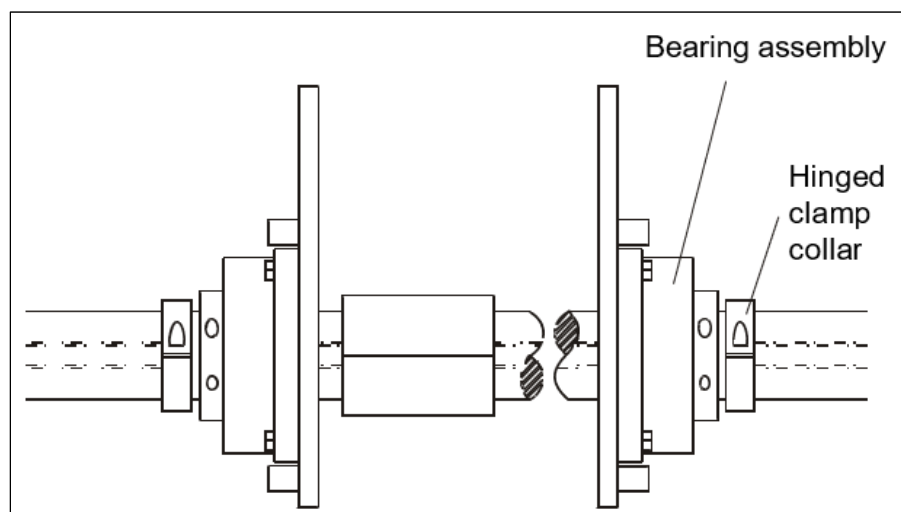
ENSEMBLE SUPPORT DE PALIER DE MONTAGE ID (GAUCHE) ET COLLIER DE FIXATION ARTICULÉ (DROITE)
